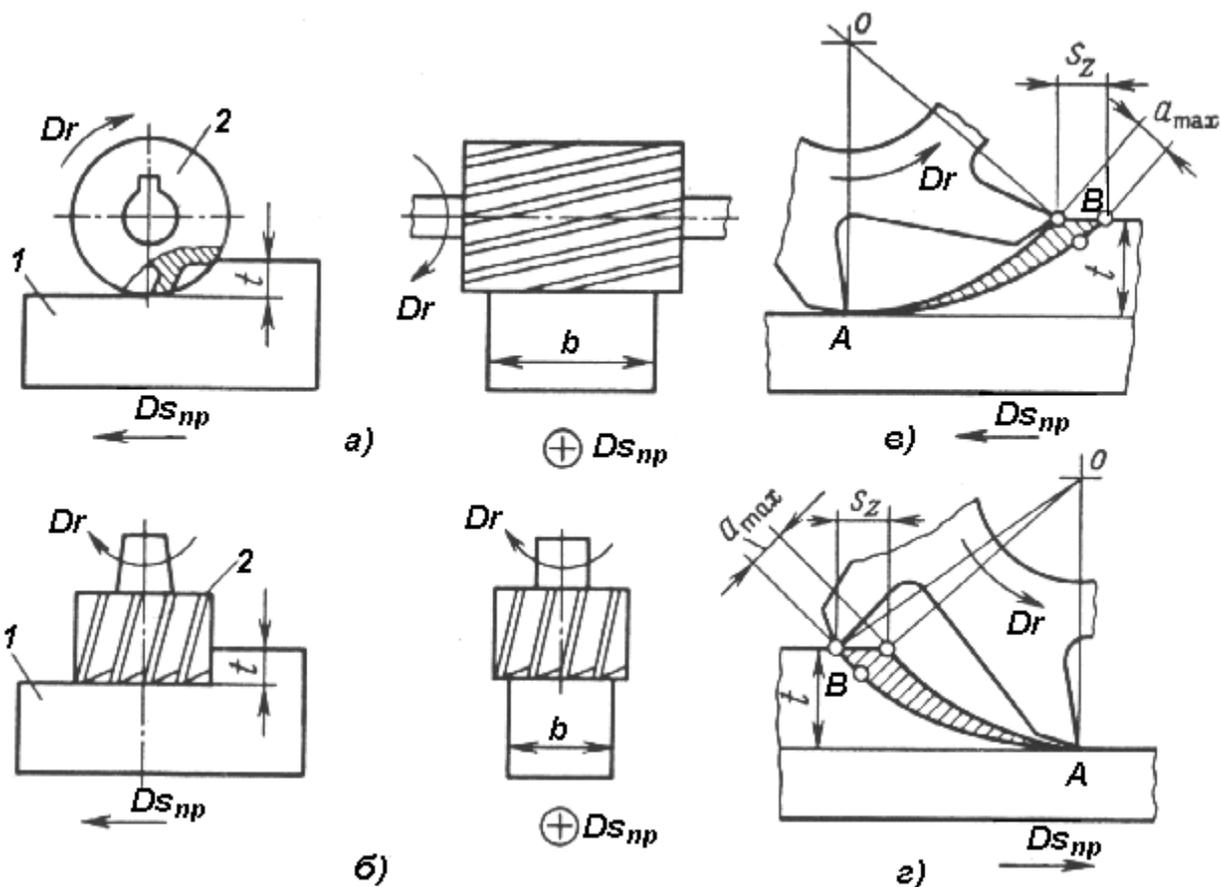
Схемы фрезерования торцевой и цилиндрической фрезами
